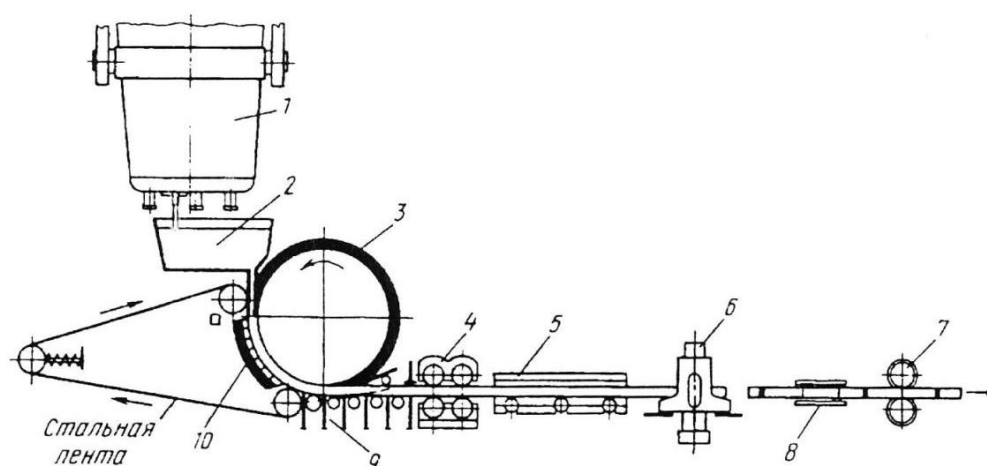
Колесно-ленточная установка для непрерывной разливки стали, совмещенная с прокатным станом конструкции *Hitachi* (Япония)
